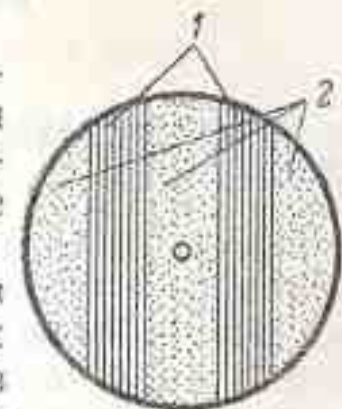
Устройство ротора реактивного синхронного двигателя:
